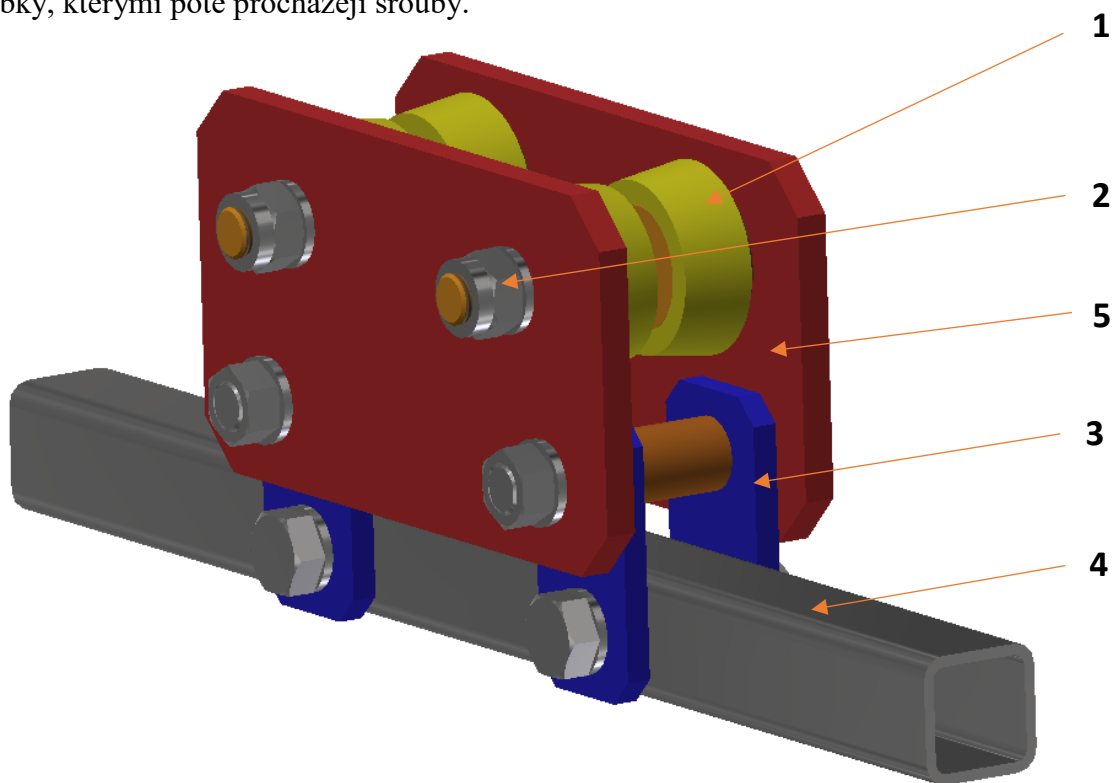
Pohled na navrženou samotnou horní konstrukci
